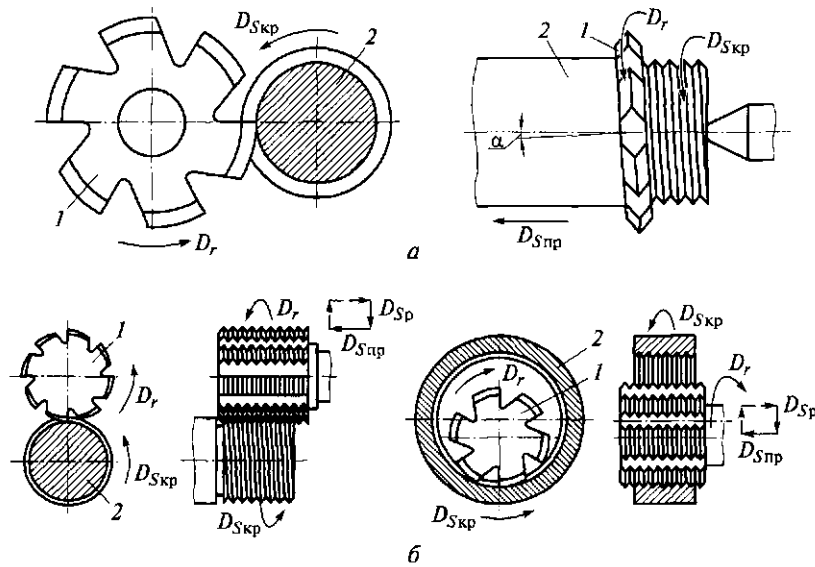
Схемы фрезерования резьб дисковой (а) и гребенчатой (б) фрезой:
